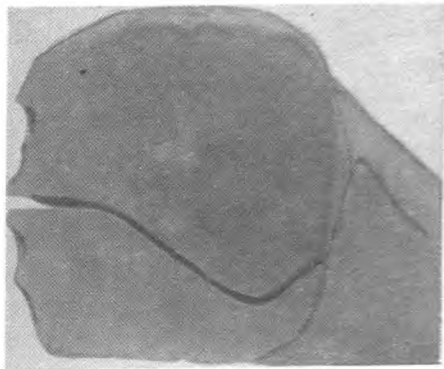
Трещины, образовавшиеся при охлаждении на воздухе заготовки из хромистой нержавеющей стали
